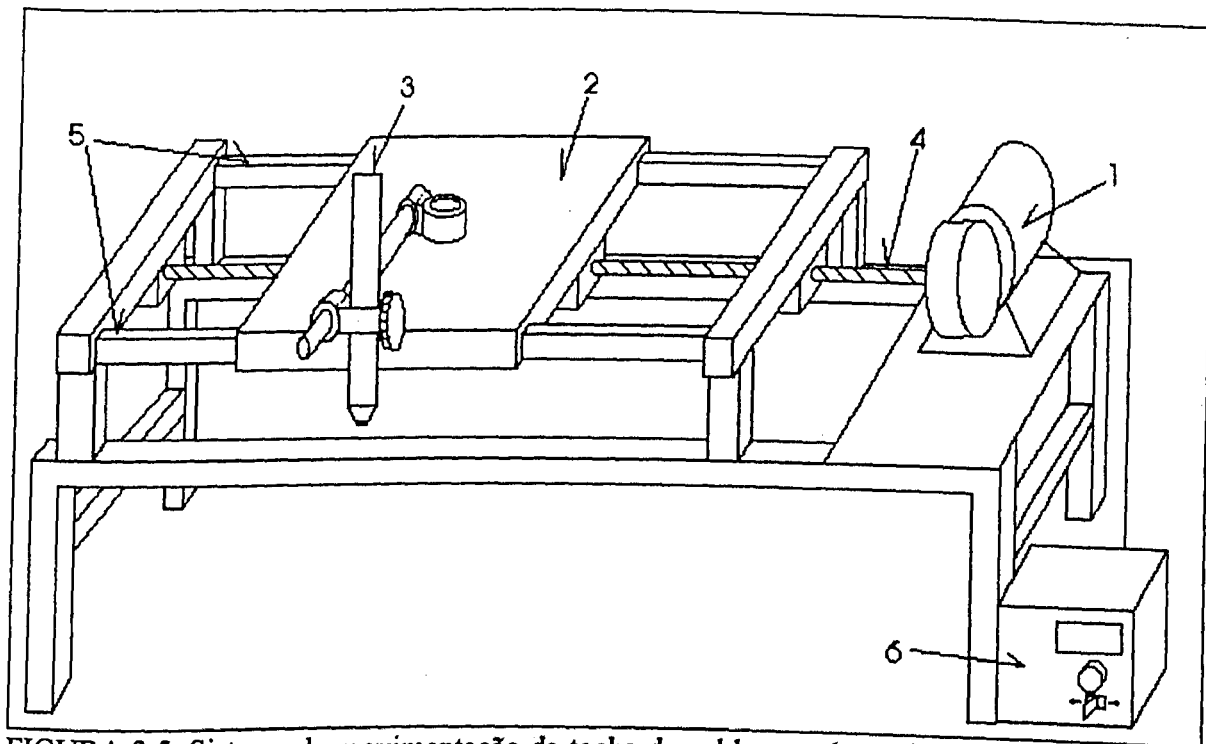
Sistema de movimentação da tocha de soldagem: 1- conjunto moto-reductor; 2- plataforma; 3- tocha de soldagem; 4- fuso; 5- guias da plataforma; 6- dispositivo eletrônico de controle de direção e velocidade de soldagem.
